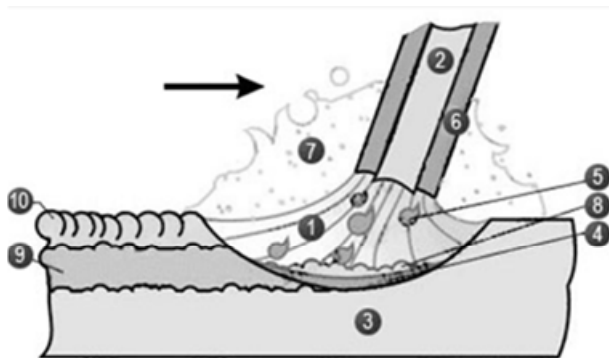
Покрытие электрода в действии: 1 – дуга, 2 – электрод, 3 – свариваемый металл, 4 – сварочная ванна, 5 – капли расплавленного электрода, 6 – покрытие, 7 – газовое облако, 8 – шлаковая ванна, 9 – сварочный шов, 10 – шлаковая корка
